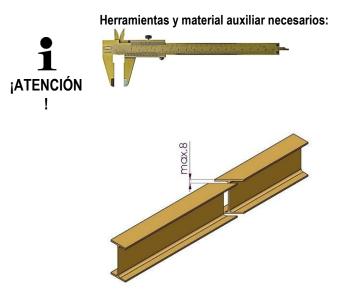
Juntas para soportes del perfil de rodadura no soldados
